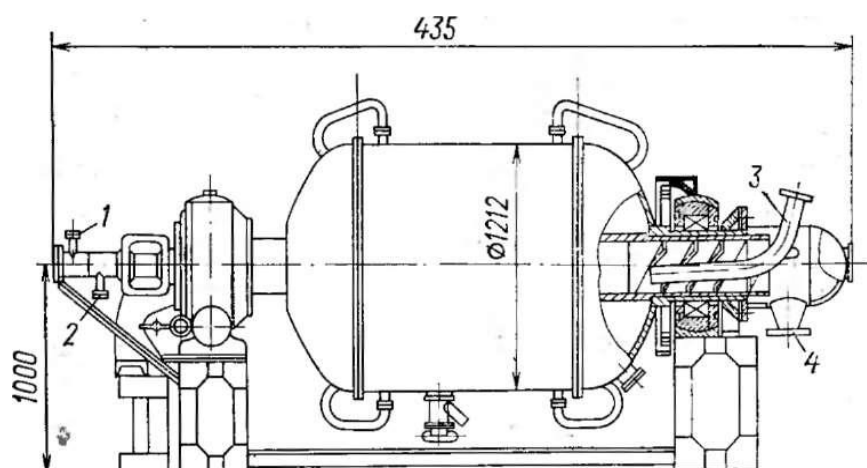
Барабанна вакуумна сушарка типу ВБС з обертвовим корпусом: 1 – штуцер для підведення пари; 2 – штуцер для відведення конденсату; 3 – патрубков для з'єднання сушарки з вакуум-насосом; 4 – розвантажувальний патрубок
